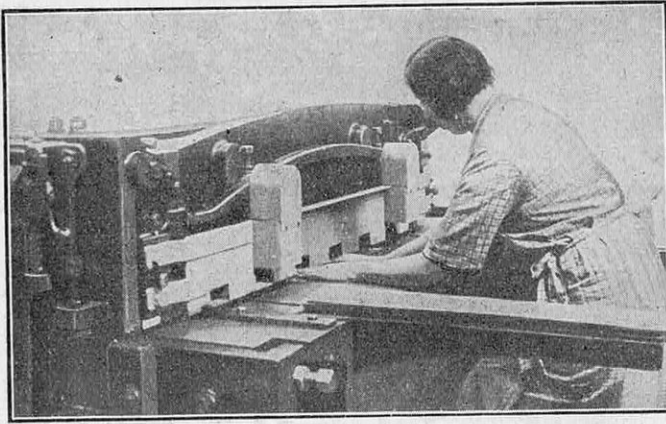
PROTECTION DES MAINS PAR UN ÉCRAN A FENÊTRES AUTORISANT LE SEUL PASSAGE DES PIÈCES SUR UNE PRESSE A ESTAMPER
